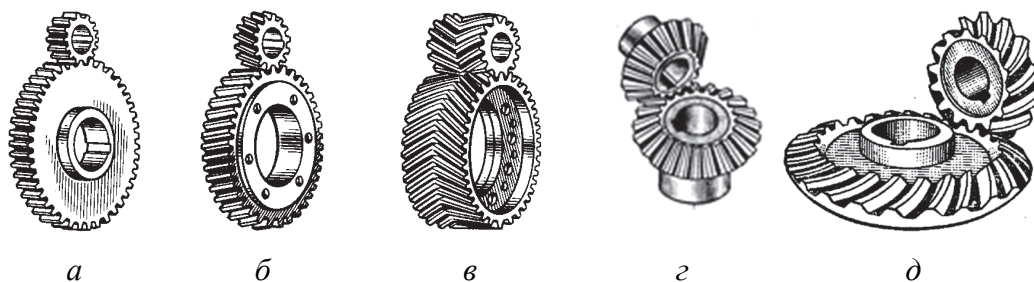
Зубчатые передачи внешнего зацепления:
